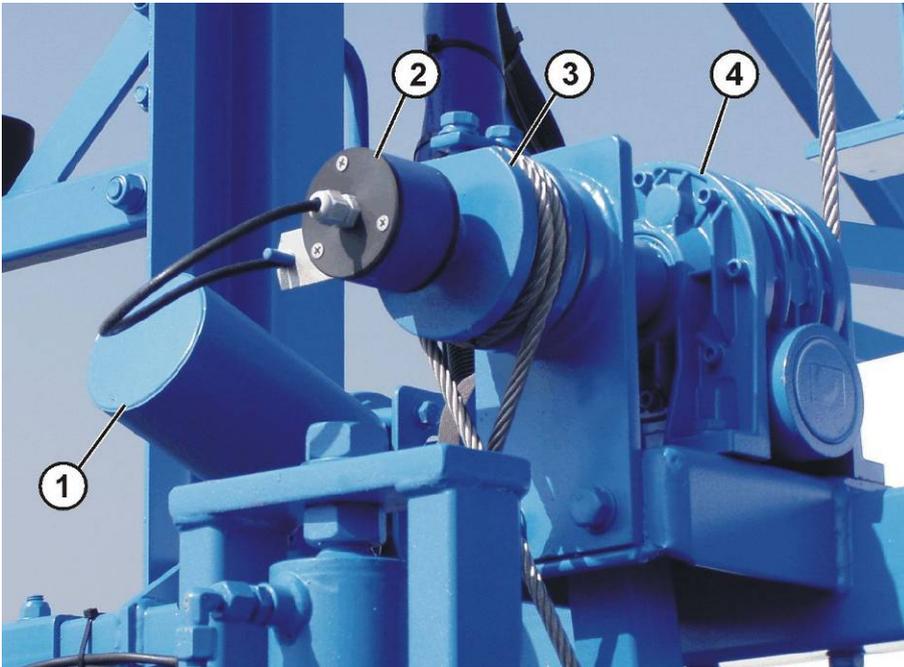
/2 Maschinenelemente - elektrisches Kippen
